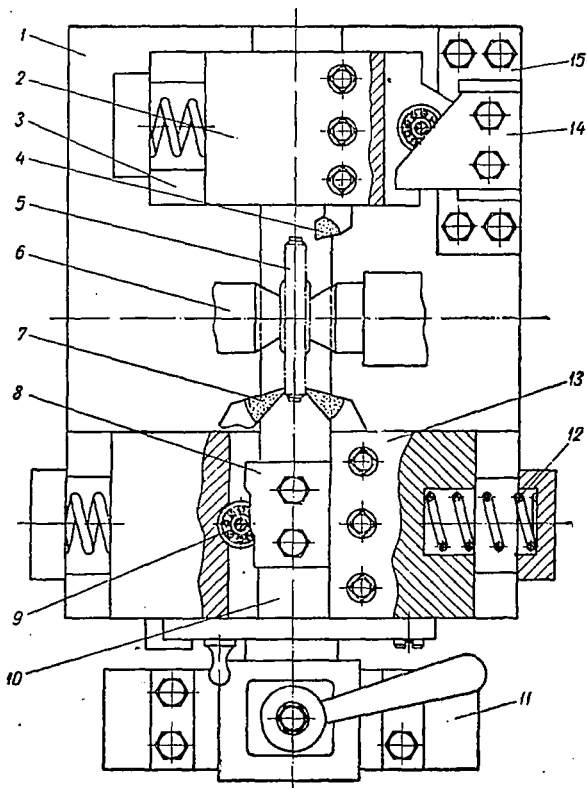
Приспособление для одновременной подрезки двух торцов и обточки детали.
